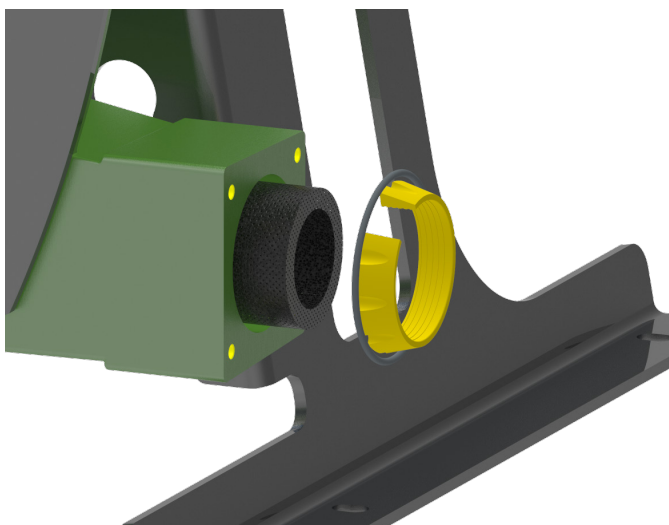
Entfernen Sie den O-Ring und den Klemmring.
